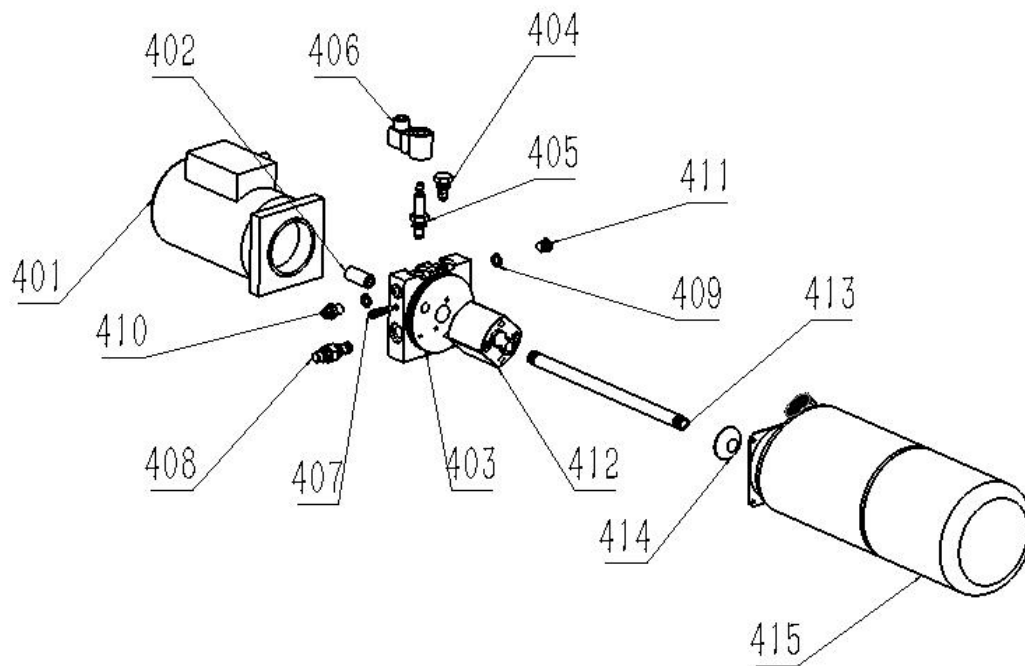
Explosionszeichnung des Hebebock-Aggregats
